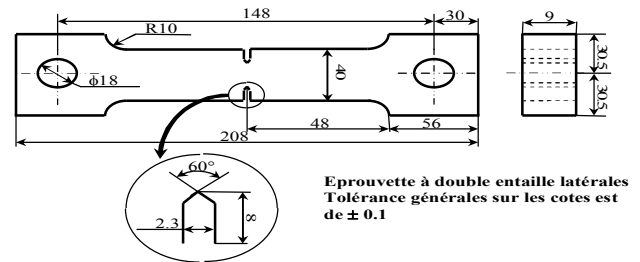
Dimensions de l'éprouvette d'étude (mm)
